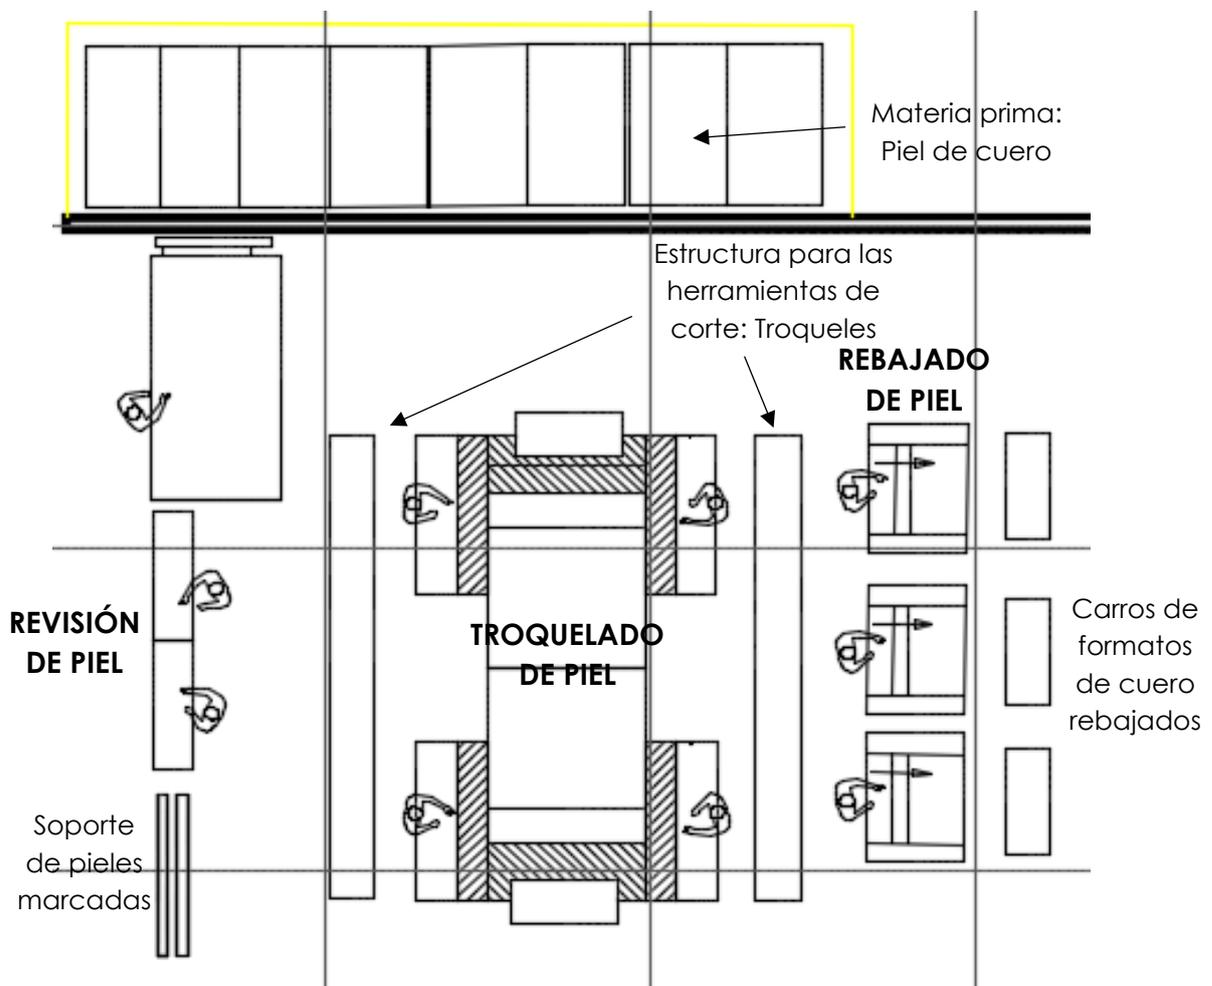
Layout actual: Zona 1. Fuente: Elaboración propia
